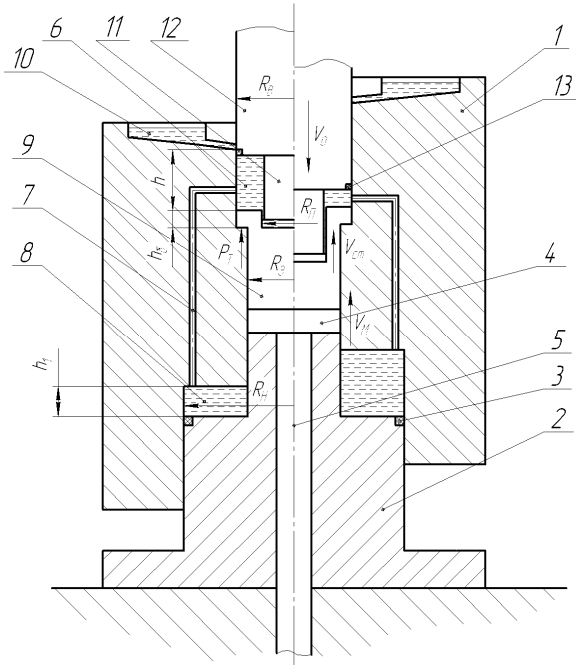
Схема штампу для видавлювання з розтягом сталевих виробів з порожниною постійного діаметру
